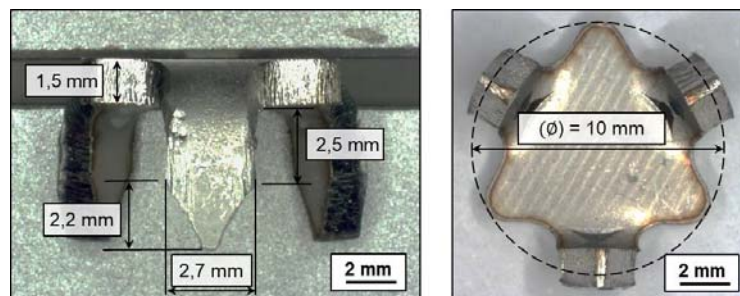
Blechelement für die Durchdringung und Schweißung
